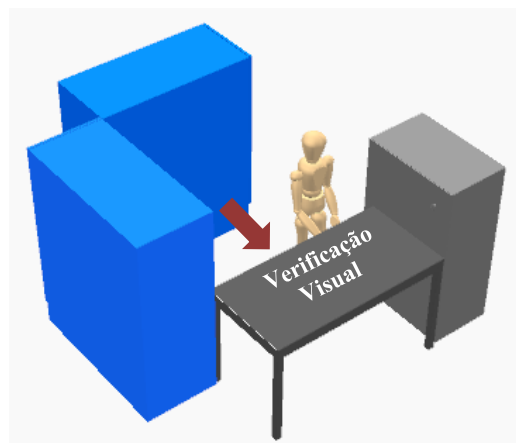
Verificação visual do bloco após a segunda soldadura.
